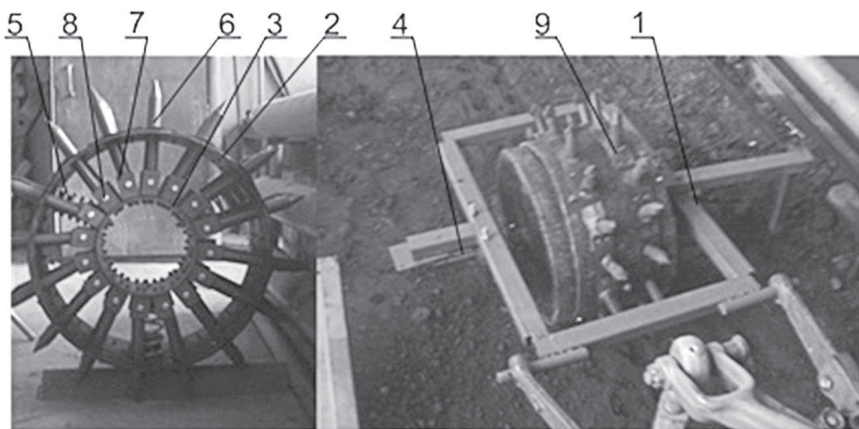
Общий вид конструкции виброкатка: 1 – рама; 2 – наружный барабан; 3 – внутренний барабан; 4 – ось; 5 – пружина; 6 – шпора; 7 – кронштейн; 8 – палец; 9 – защитный кожух
